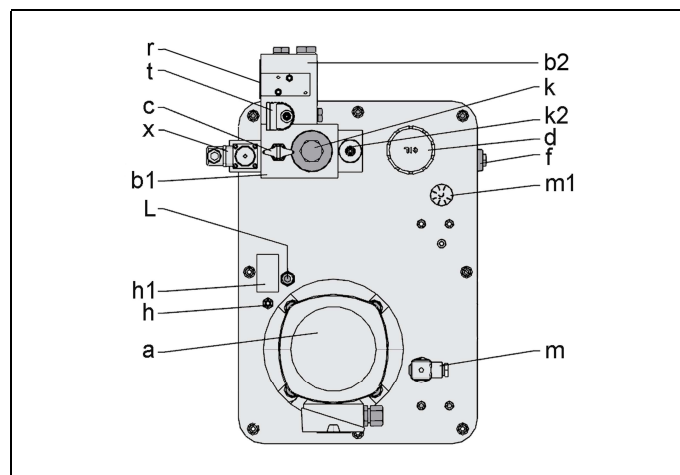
Figure couvercle du groupe hydraulique V27/ V40/ V63
